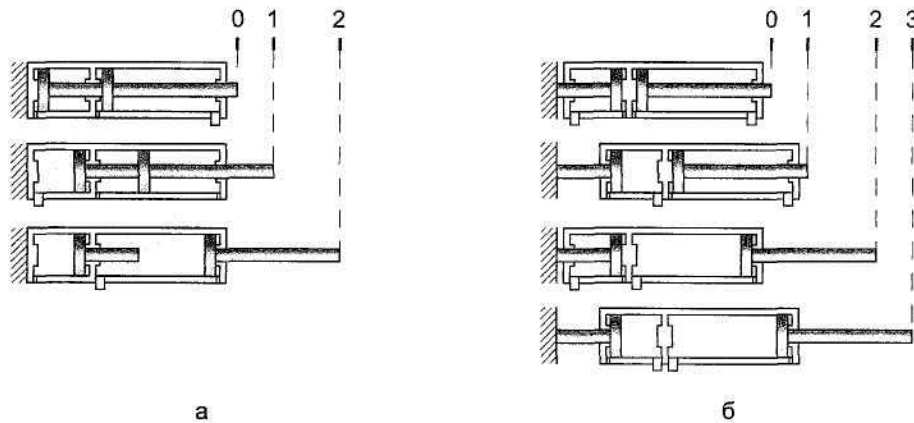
Багатопозиційні пневмоциліндри:
